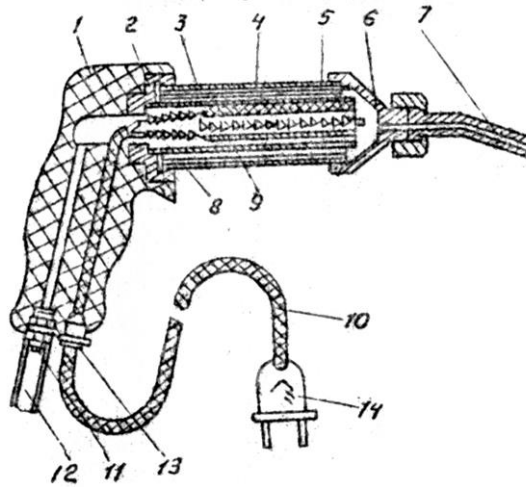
Схема сварочного пистолета: 1 – рукоятка; 2 – вставка; 3 – обойма; 4 – изолятор; 5 – стакан; 6 – колпак; 7 – сопло; 8 – бусы изоляционные; 9 – нагревательная спираль; 10 – шнур; 11 – штуцер; 12 – трубка для подвода газа
